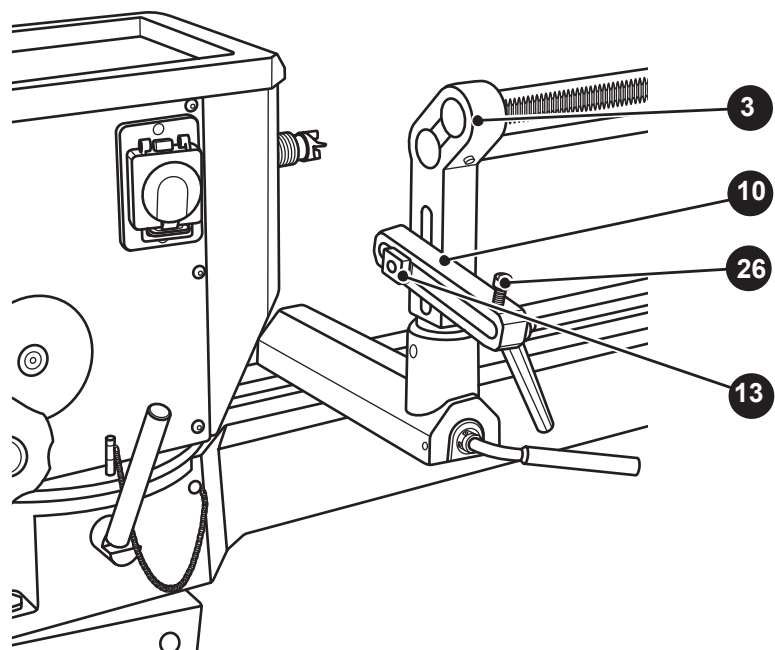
Рисунок I — установка защитного экрана и резца. Соединение суппорта копирующего устройства с кронштейном.
